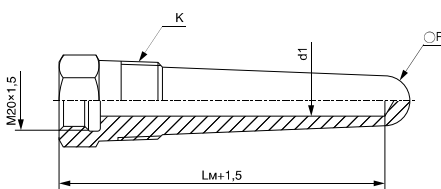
ГТ-712 коническая с конической резьбой для ДТ с неподвижным штуцером
